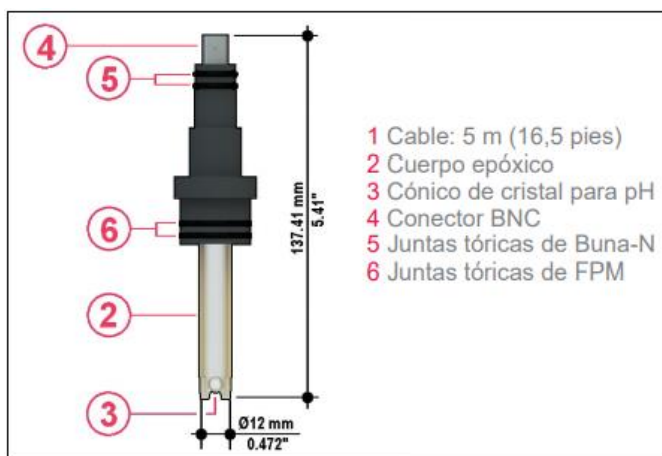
Electrodo FLS pH/ORP 200, Plano constructivo.
